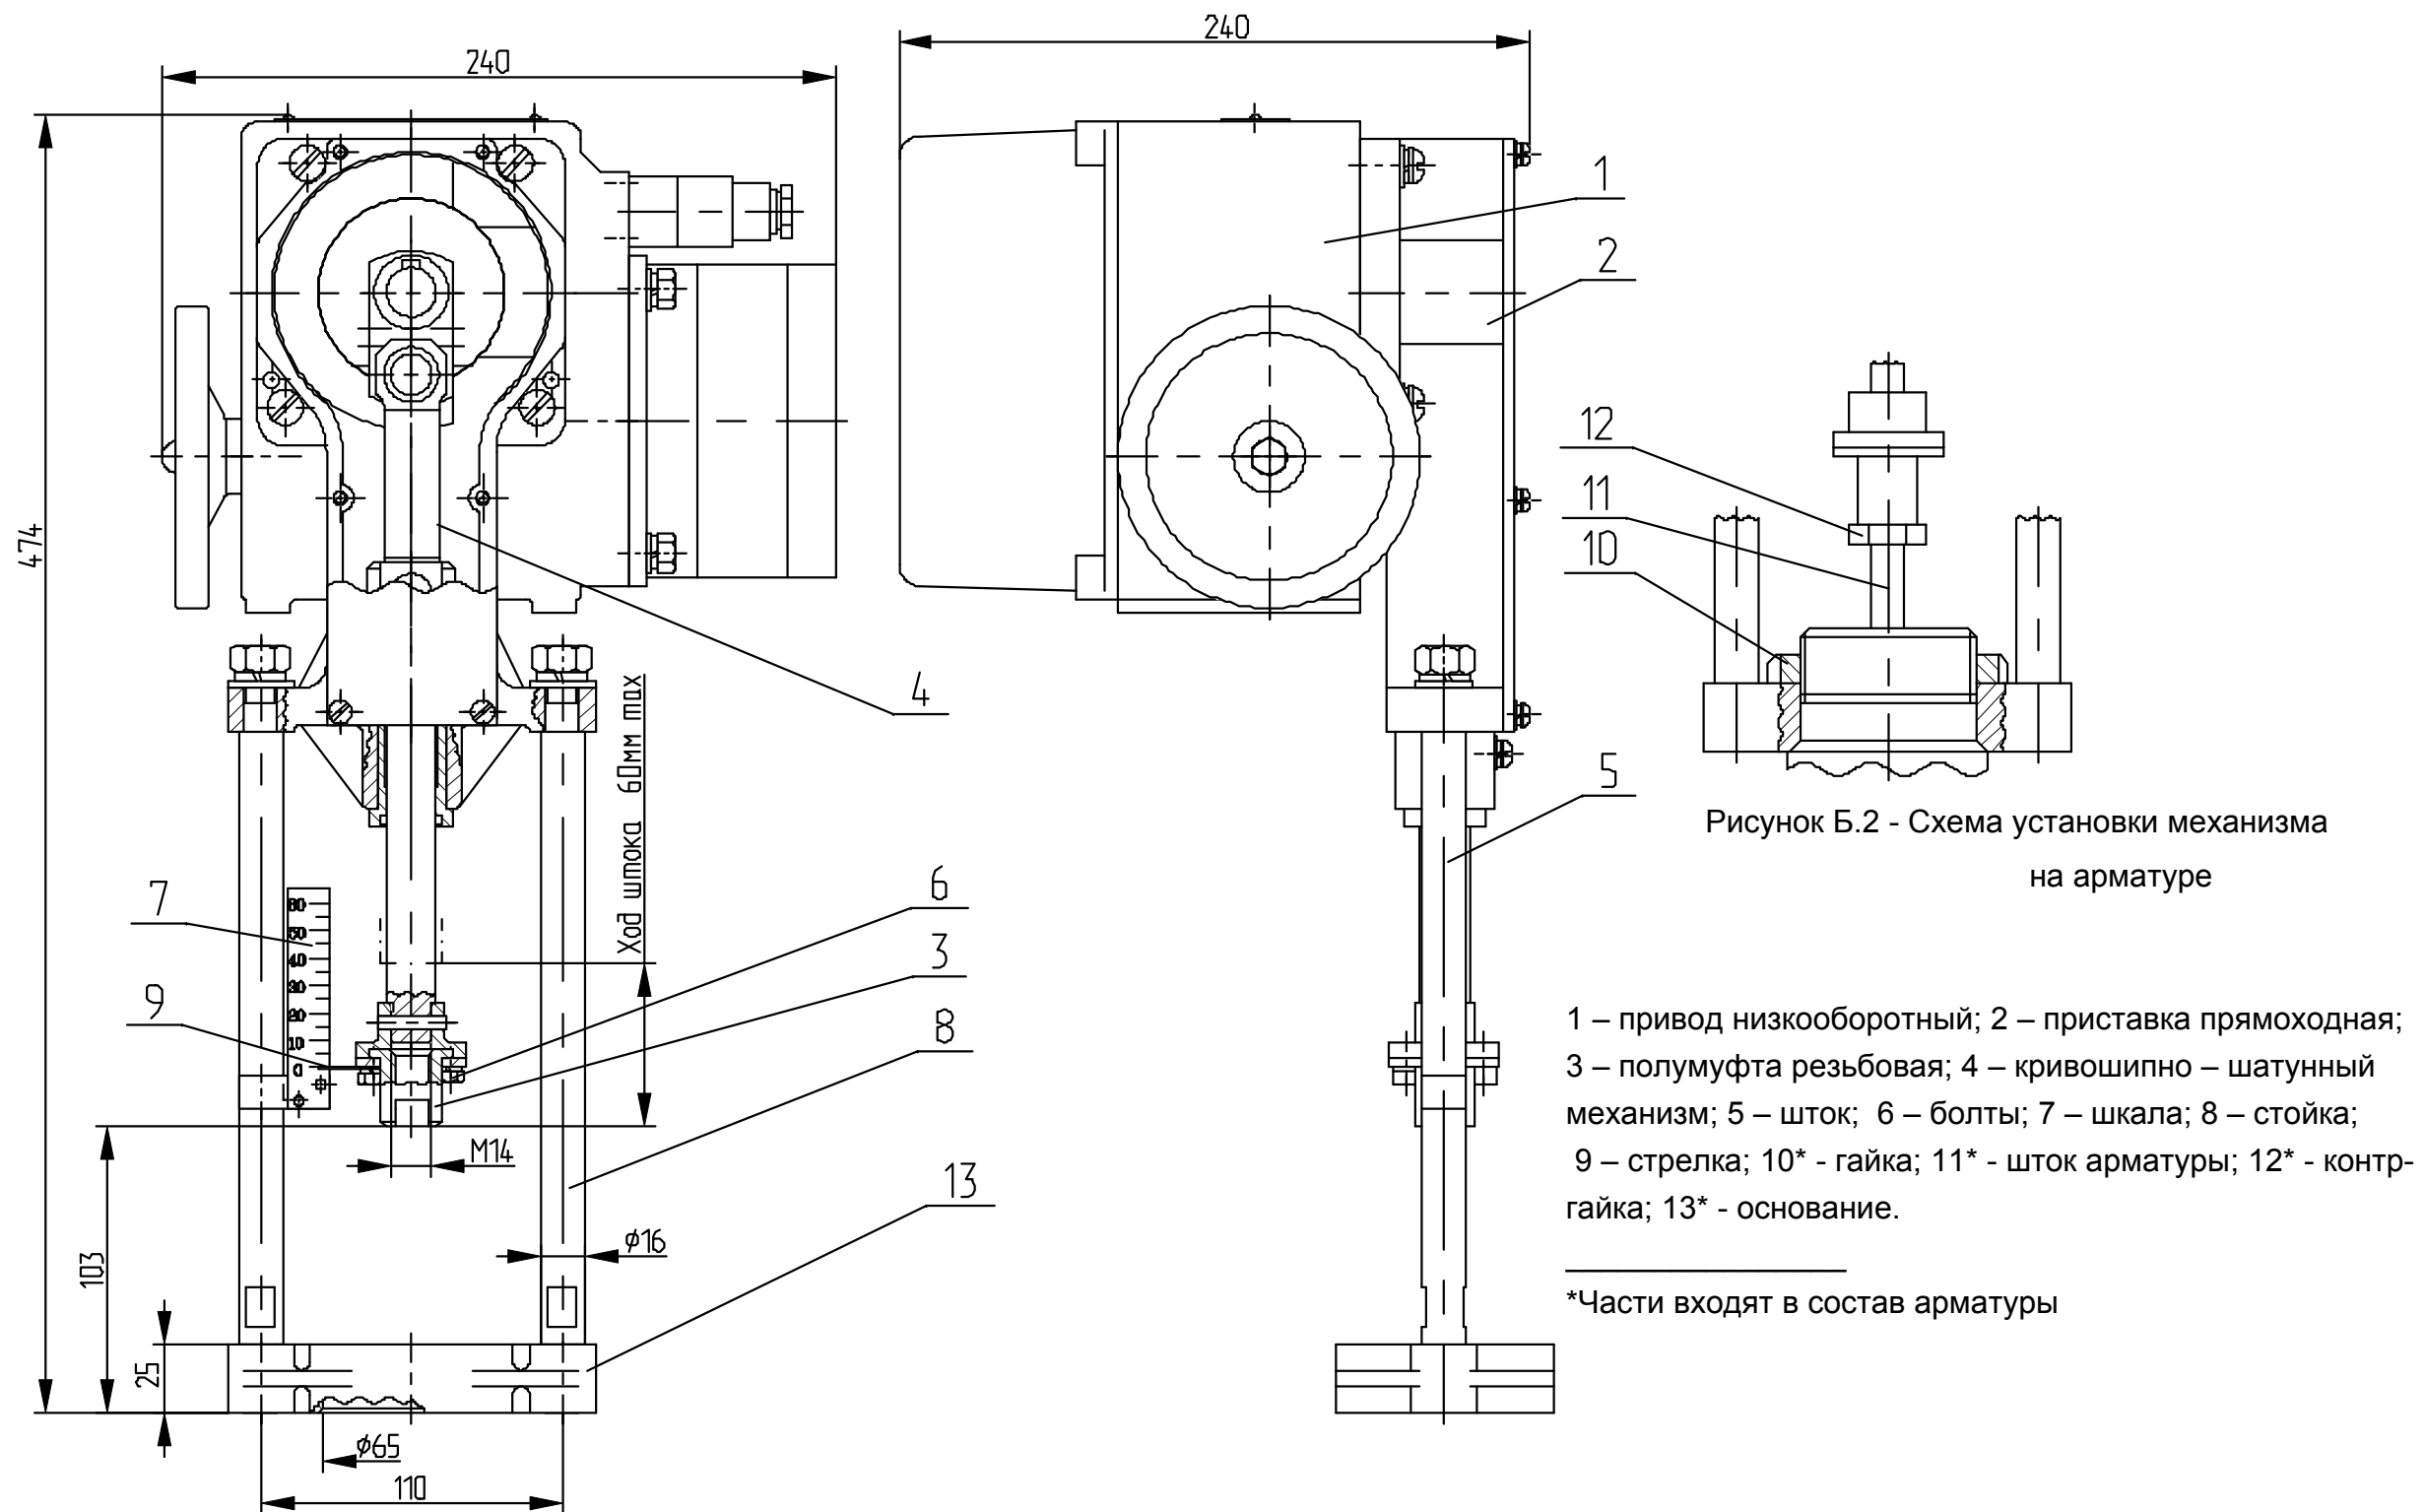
Общий вид, габаритные и присоединительные размеры механизма МЭПК-99
